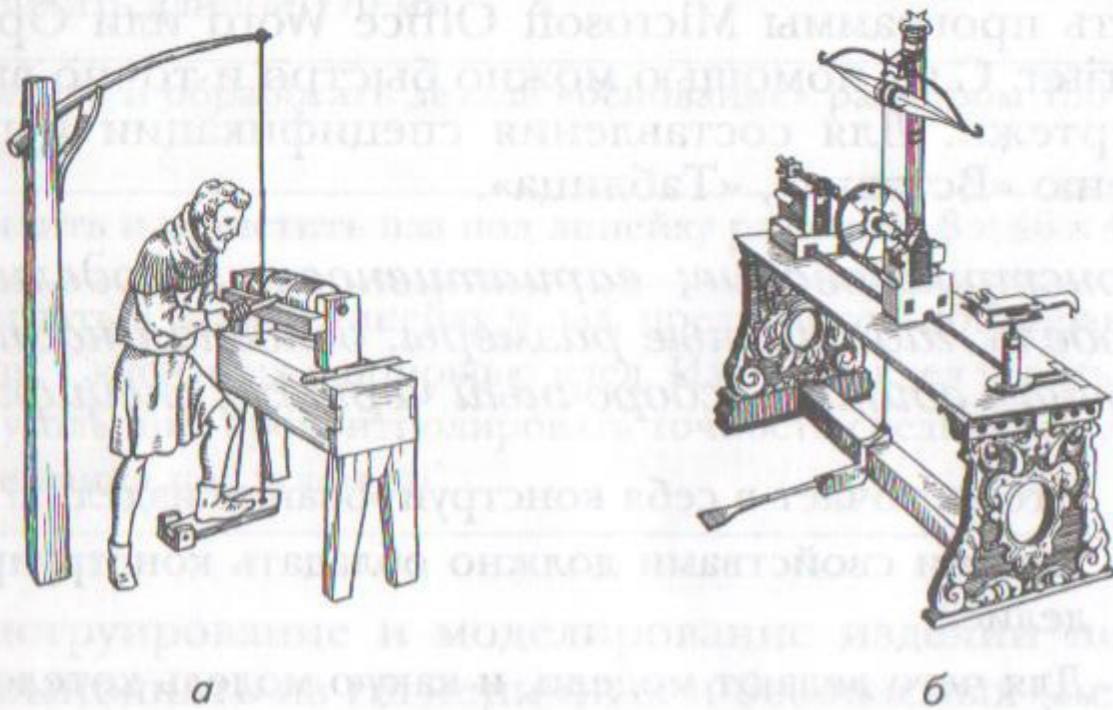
Токарные станки: а — средневековый станок; б — станок Нартова
